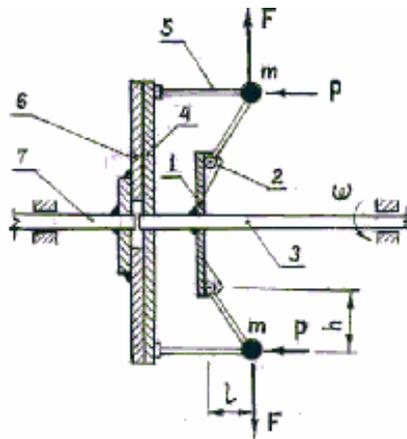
Схема сцепления карданного вала с валом двигателя
